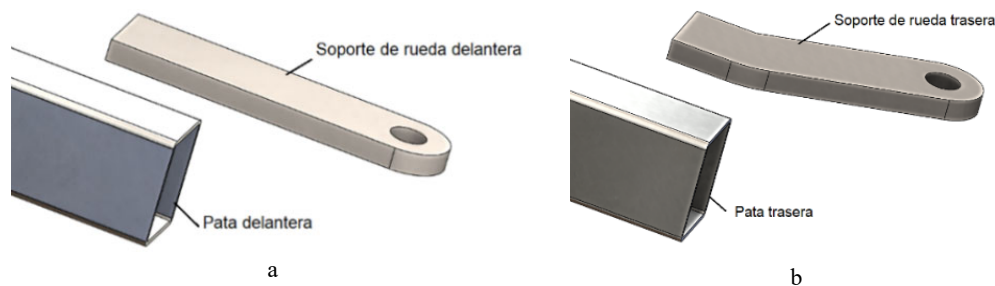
Disposición de soporte de ruedas a) delanteras, b) Traseras.
